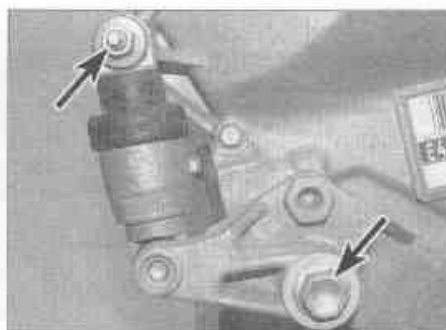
Отверните гайку, выверните болт (отмечены стрелками) и снимите натяжитель ремня привода вспомогательных агрегатов
